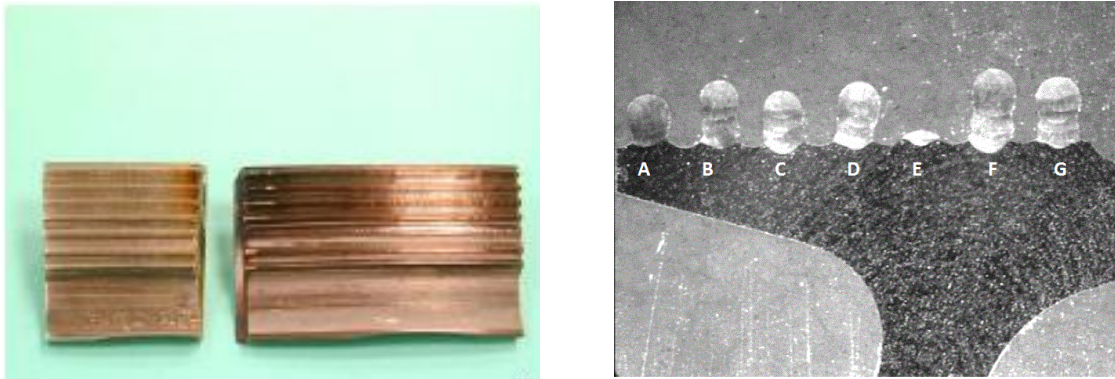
Sección transversal del cierre de cuchillas soldado
